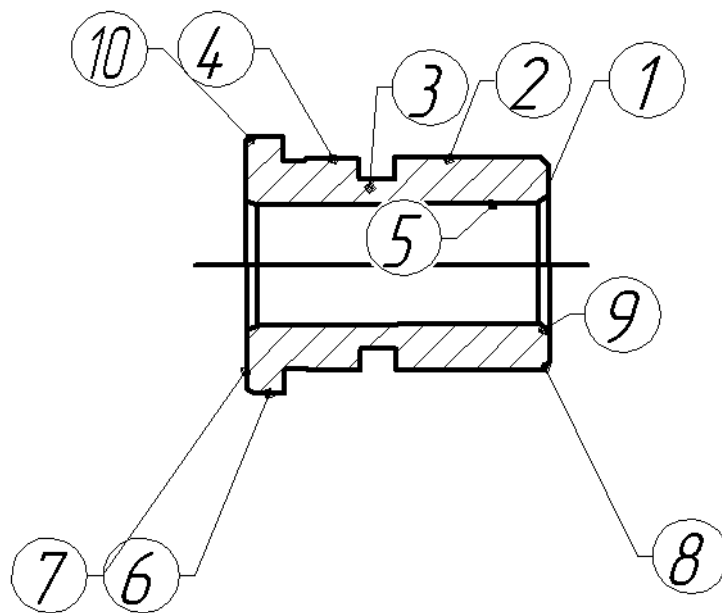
Нумерація оброблюваних поверхонь деталі Втулка
